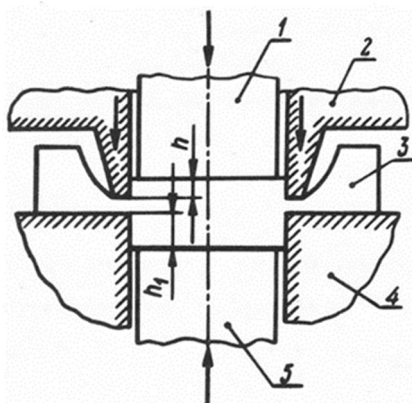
Схема чистовой вырубki листовых металлов встречными матрицами
